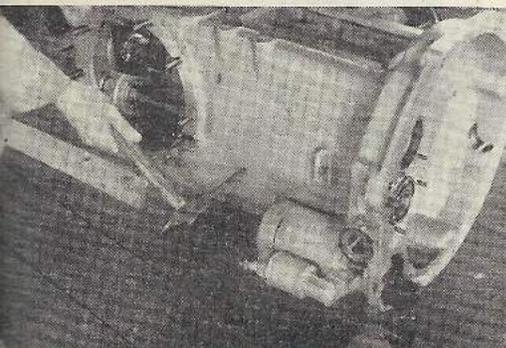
Zum Ausbau des Laufrades im Getriebe muß der Schwerverspannstift zurückgeschlagen werden.
